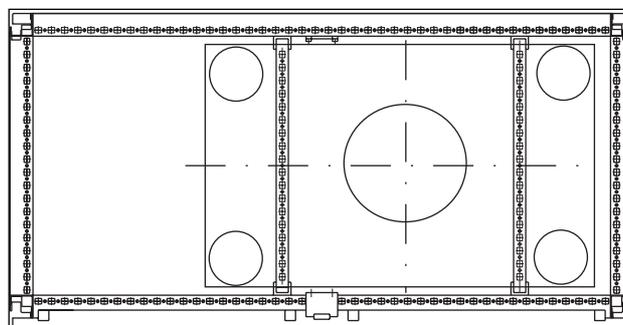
Rinforzo della lamiera del tetto nell'armadio TS 8
